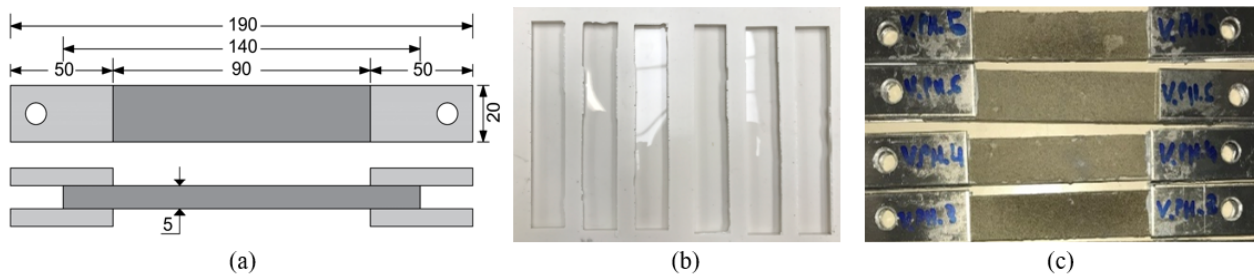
(a) Géométrie de l'éprouvette, dimensions en mm ; (b) Moule de silicone utilisé et (c) Eprouvettes de traction parallélépipédiques
